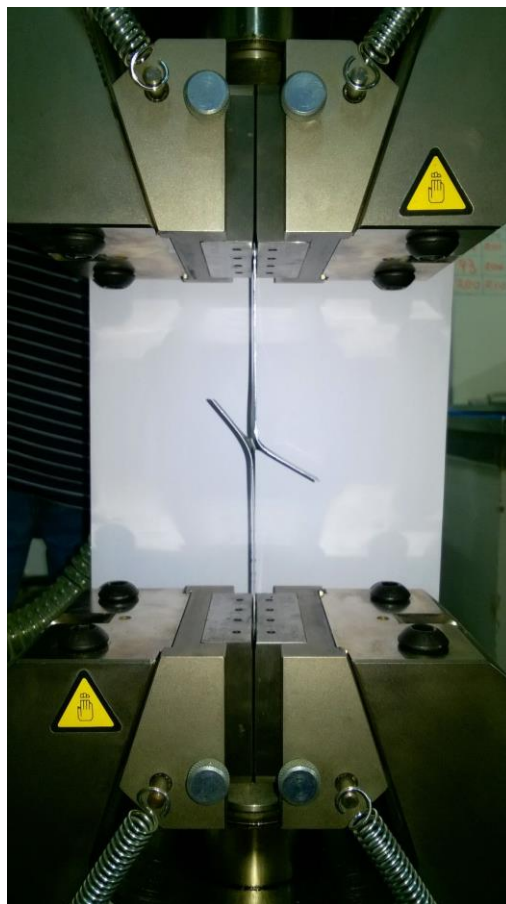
Perfil do corpo de prova após o ensaio nas juntas soldadas.
